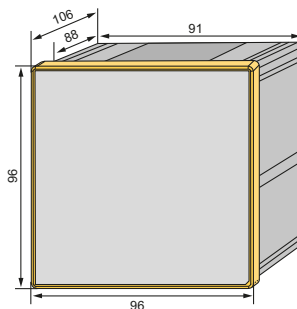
Maßbild PEM533 (Frontansicht)
